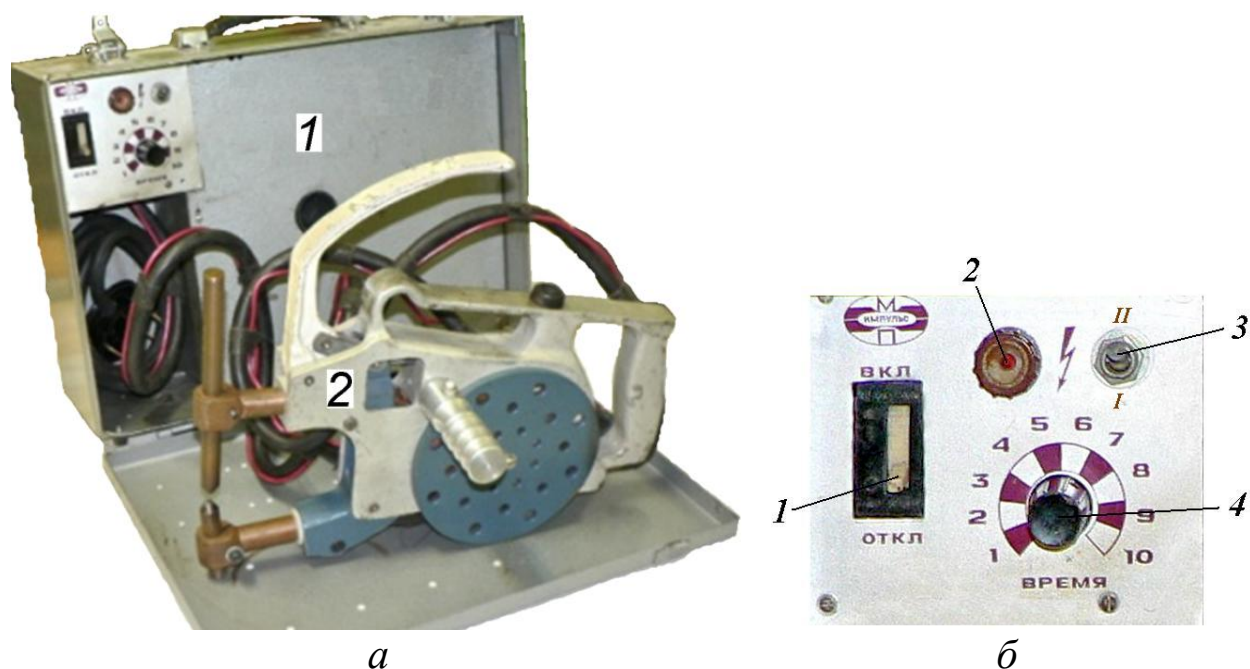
Универсальный переносной ручной аппарат для контактной сварки с инверторным источником питания: *а* – внешний вид; *б* – панель настройки режима сварки (обозначения в тексте); 1 – инверторный блок питания; 2 – клещи
